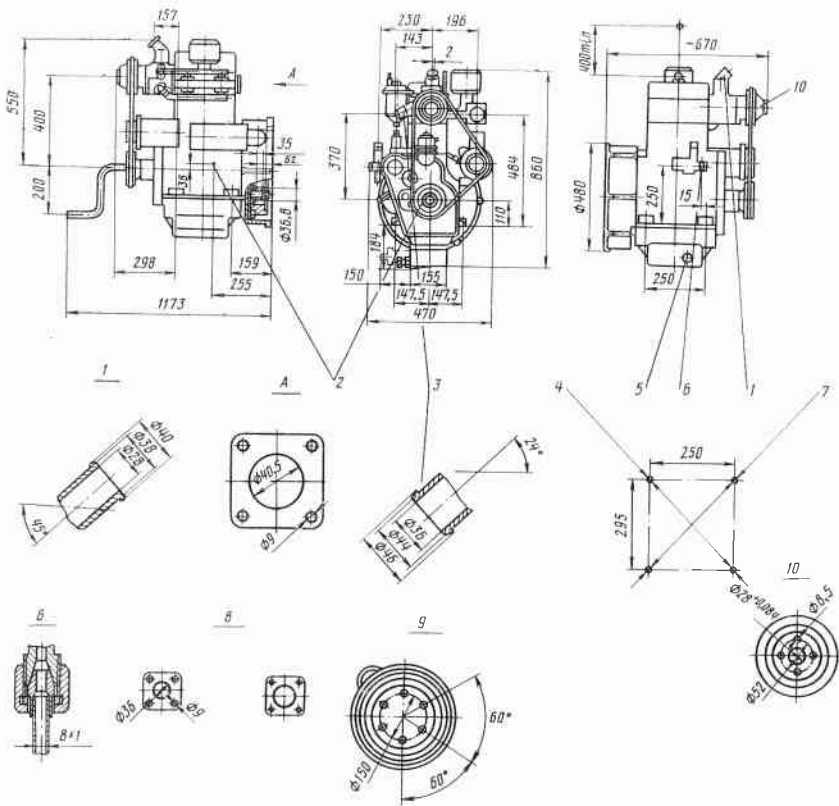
Габаритный чертёж дизелей П12, П21, П22:
